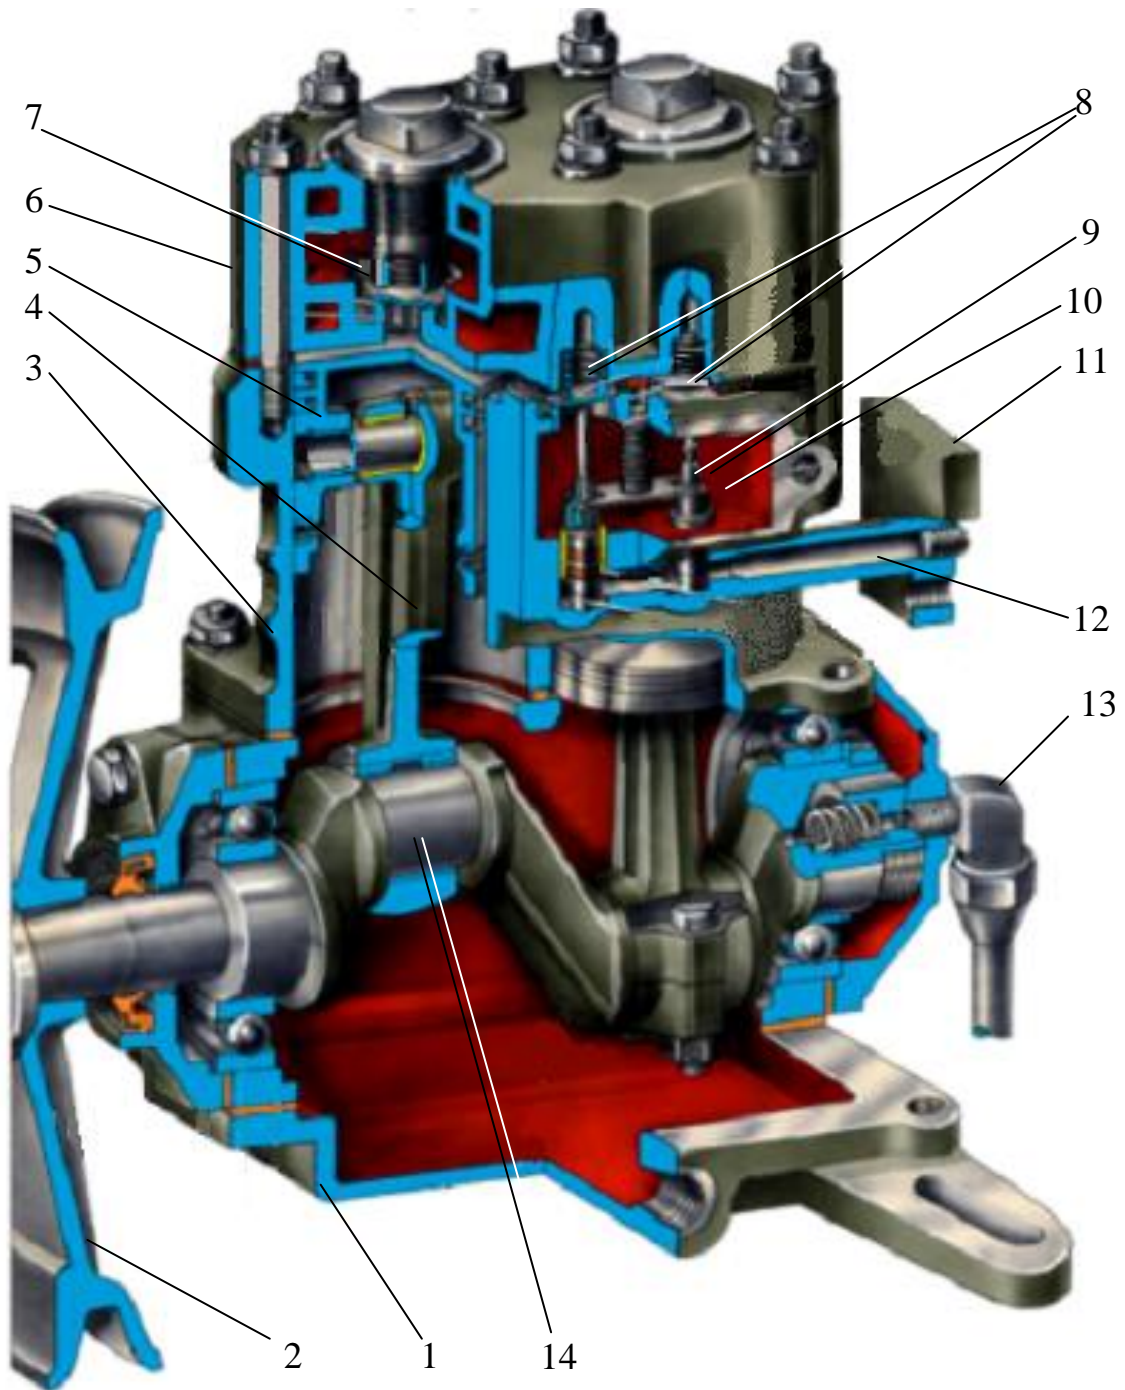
Компрессор: 1 – картер; 2 – шкив; 3 – блок цилиндров; 4 – шатун; 5 – поршень; 6 – головка блока; 7 – нагнетательный (выпускной) клапан; 8 – впускные клапаны; 9 – плунжер регулятора давления; 10 – впускной канал; 11 – фланец крепления регулятора давления; 12 – канал от регулятора давления; 13 – штуцер подвода масла из системы смазки двигателя; 14 – коленчатый вал
